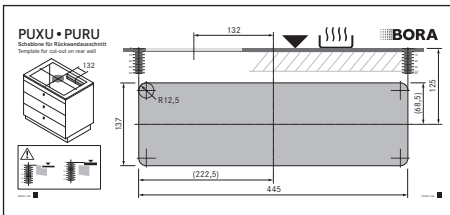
Dimenzije vgradnje pri obtočnem zraku, različica montaže A
